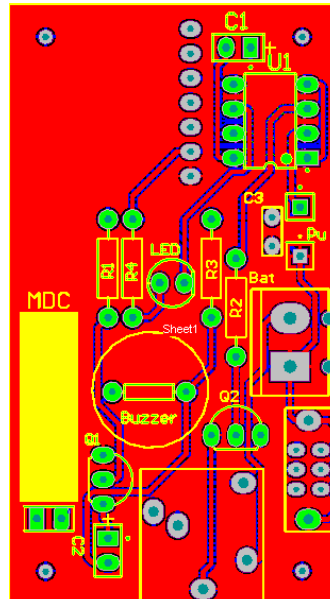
Diseño electrónico de la PCB del dispositivo de la alternativa 1.
